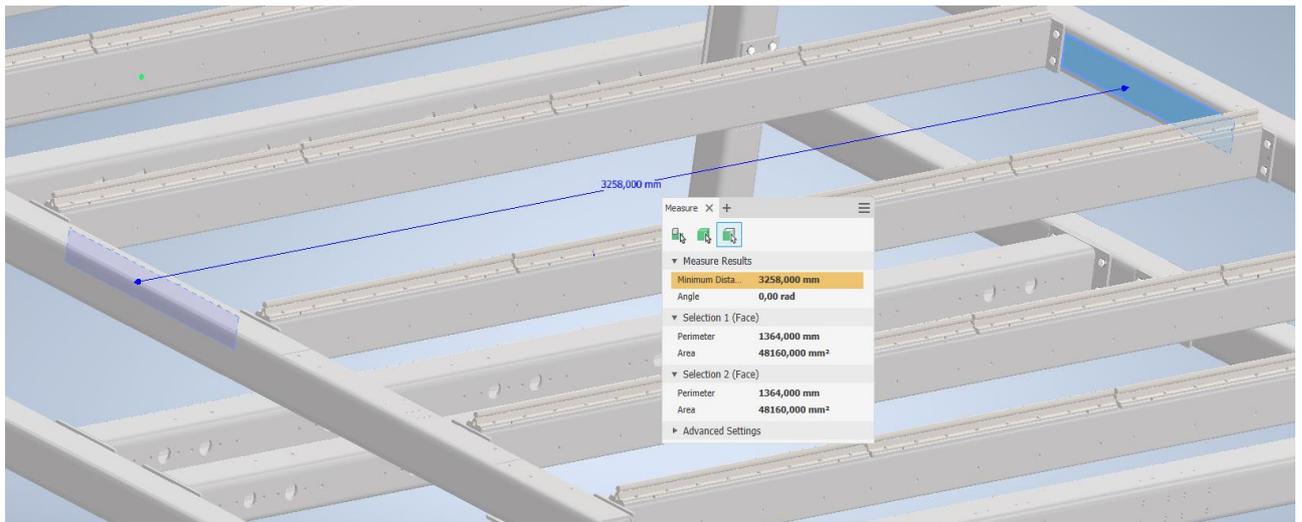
Comprimento da máquina a adaptar (3258 mm)
